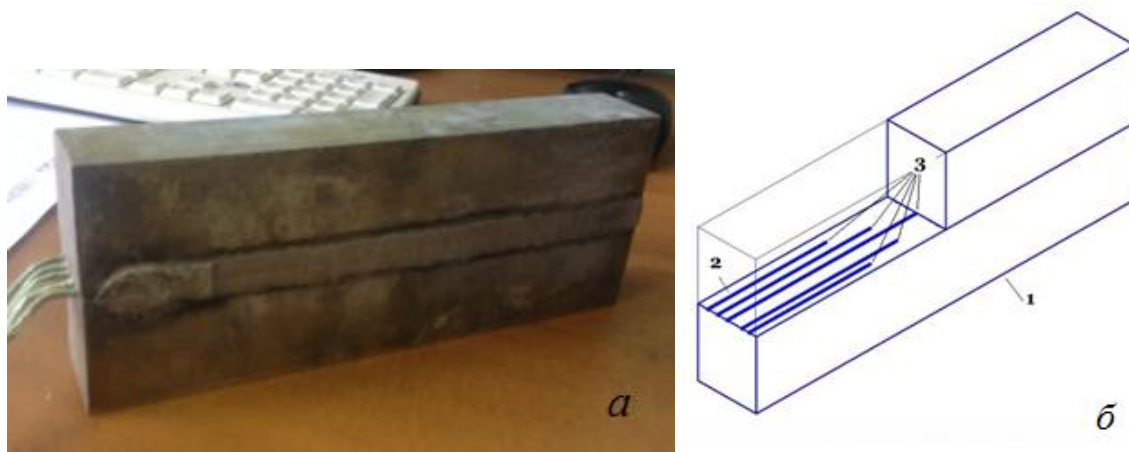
Опытный образец (а) и схемой (б), термопарами 1 расположенными в пазах размерами 1*1 мм для установки термодпар – 2 по толщине образца, пазы расположены вдоль образца. Горячие спаи термодпар приварены контактной сваркой в местах – 3 и расположены таким образом, что не оказывают влияния на перемещение изотермы по толщине образца
